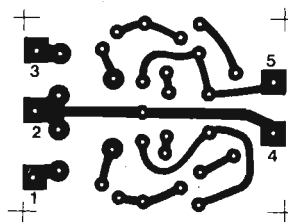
Disegno al vero del circuito stampato che il lettore dovrà comporre prima di eseguire il montaggio dell'indicatore di livello BF.
